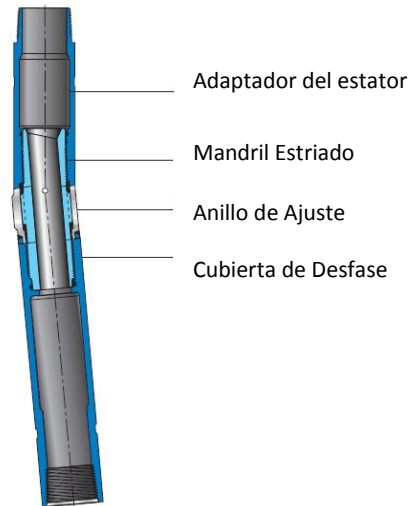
Bent housing* ajustable. Modificado ^[11]
